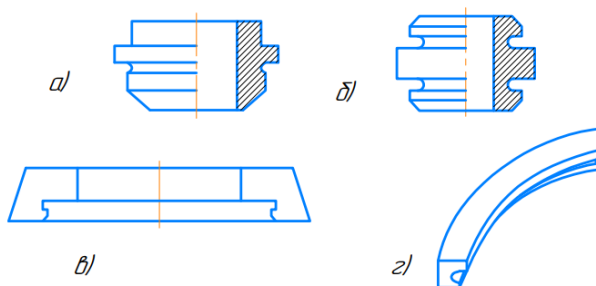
Конструкція закатувальних інструментів: а) ролик з канавкою на зовнішній поверхні; б) з двома робочими канавками; в) ролик з робочою канавкою на внутрішній поверхні; г) закатувальна дуга.
